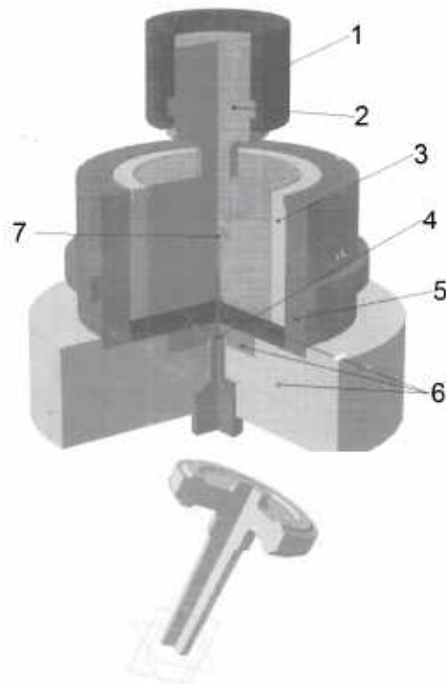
Штамп для формоутворення поковки типу стрижень з фланцем
